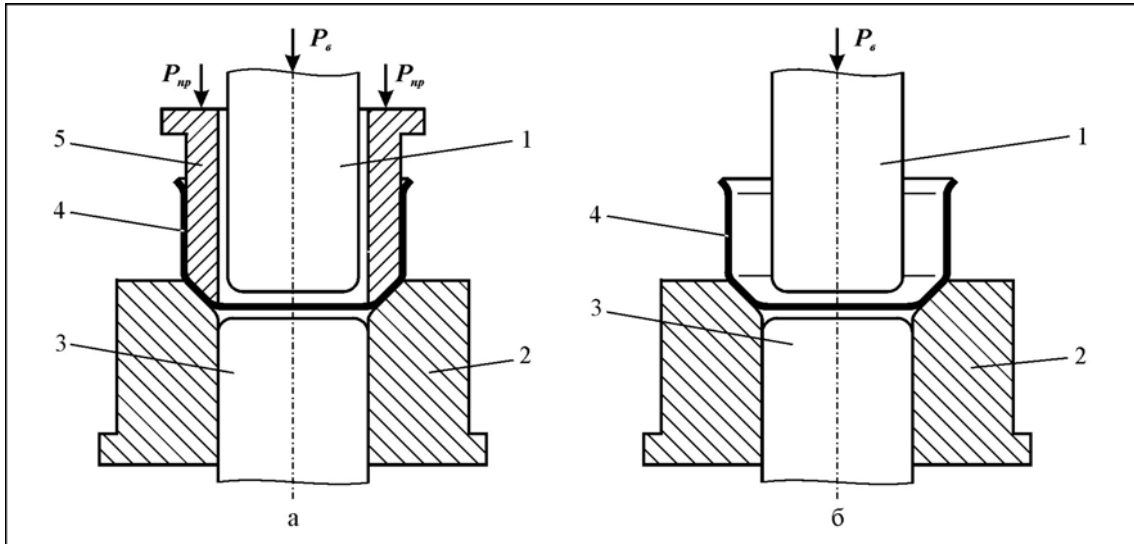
Схеми штампів для подальшого витягування (початкова фаза штампування): а – з притиском порожнистої заготовки; б – без притиску порожнистої заготовки; 1 – пуансон; 2 – матриця; 3 – виштовхувач; 4 – порожниста заготовка; 5 – притискач
